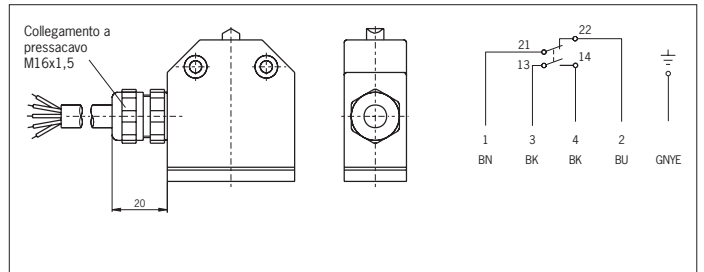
Dimensioni/schema di collegamento SN01.558X... con cavo di collegamento (cavo PUR, 5x0,5 mm²)
